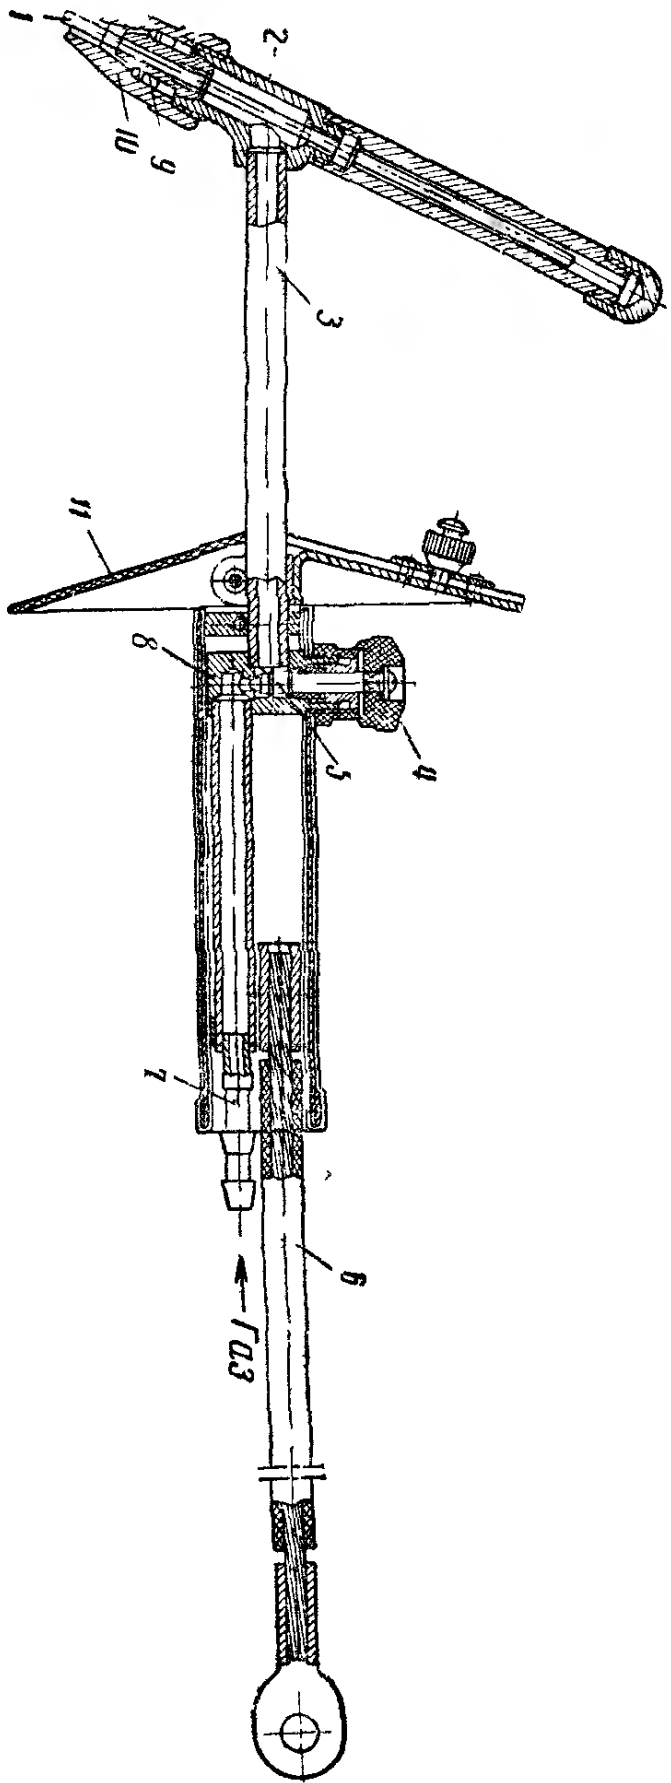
Сварочная горелка для аргоно-дуговой сварки
